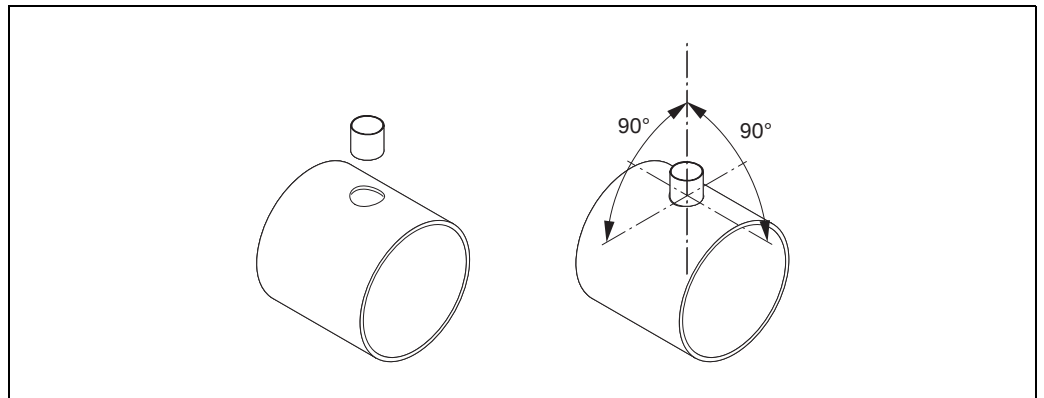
Positionierung des Schweißstutzens auf dem Rohr (oder Kanal)
